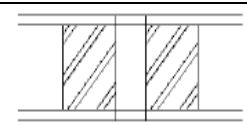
Řez sendviče s insertem „Cold bonded“ [15]
